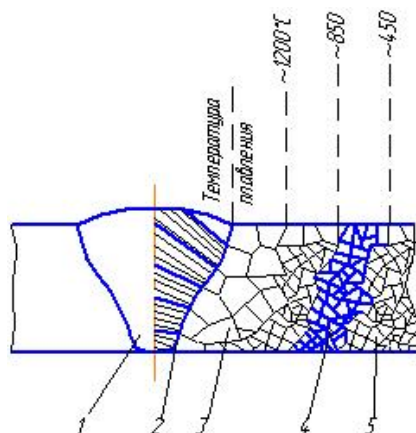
Схема структурных зон сварного соединения аустенитной стали: 1 – металл шва; 2 – линия сплавления; 3 – зона роста зерна; 4 – зона возможного распада аустенита; 5 – основной металл
